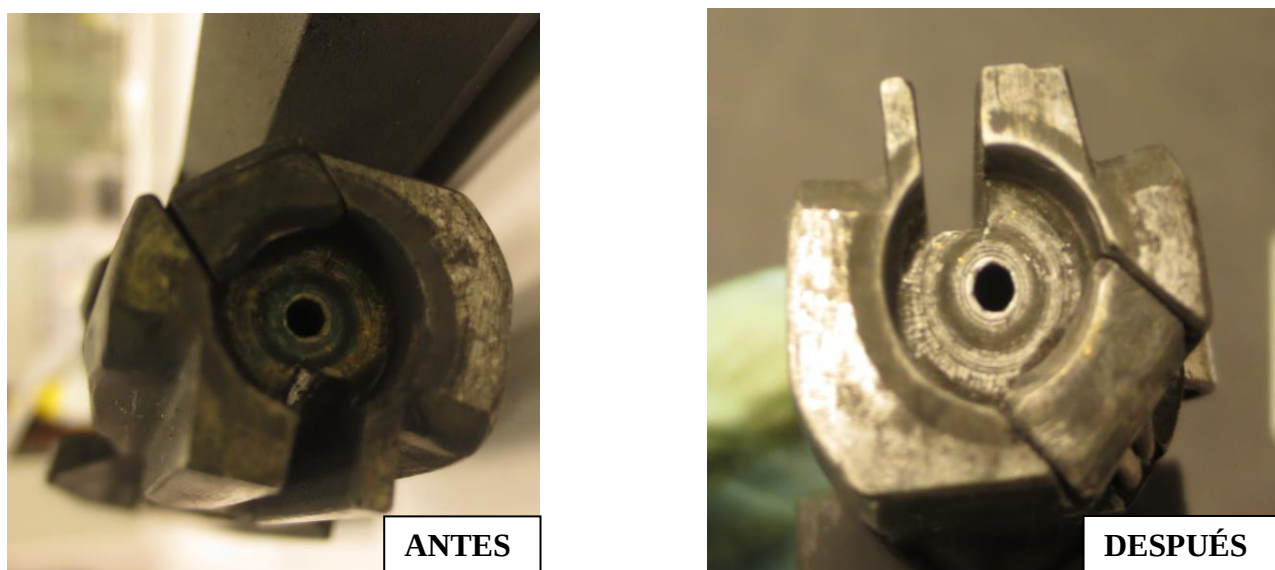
Vista frontal del cierre de un fusil CETME antes y tras su limpieza
